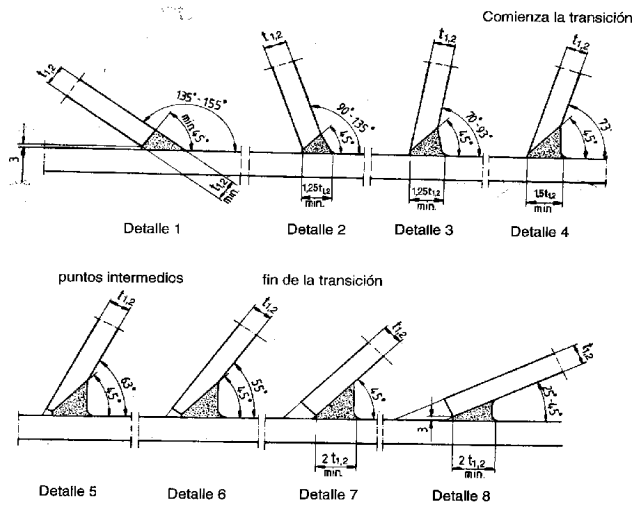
Uniones de perfiles tubulares soldados
